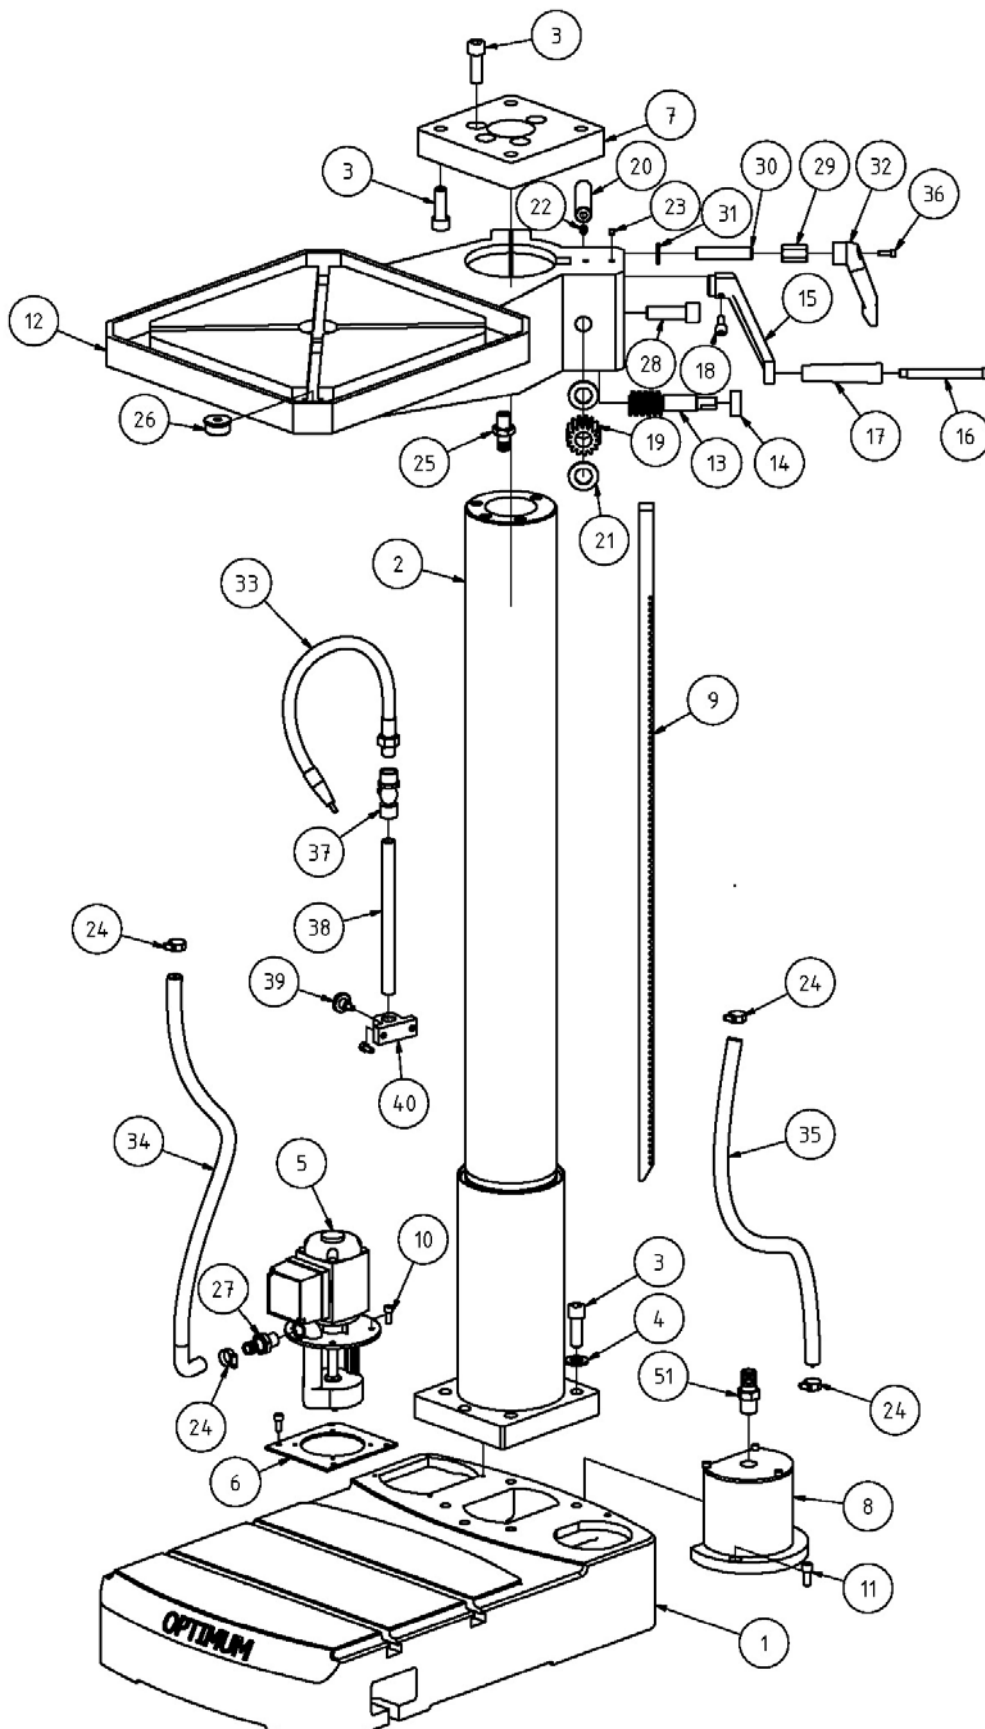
Bohrtisch - Mesa de taladro - DH 32 GS
